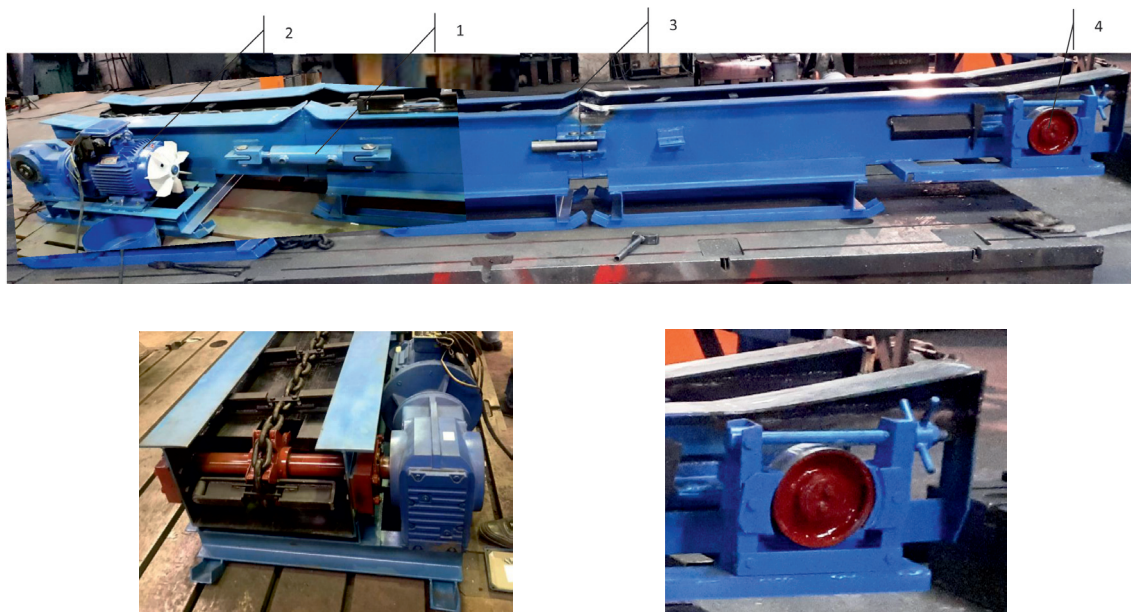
Нагрузочное устройство на полноразмерном макете комплекса приводного, поворотного и натяжного рештаков: а) общий вид: гидродомкрат поворота 1, мотор-редуктор 2, наклонно-подъемные борты, ИН 4 3; б) вид со стороны привода; в) нагрузочное устройство с тормозными колодками и винтом
